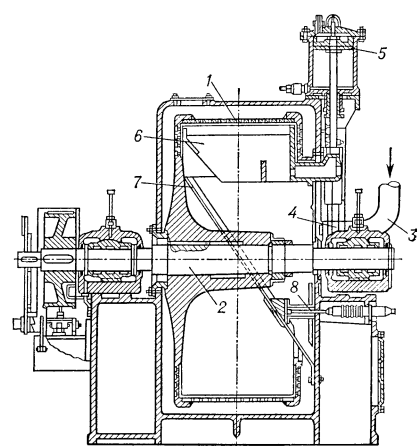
Разрез горизонтальной автоматической фильтрующей центрифуги: 1 — ротор; 2 — горизонтальный вал; 3 — труба для подачи суспензии; 4 — клапан для периодической подачи суспензии; 5 — масляный цилиндр для автоматического подъёма и опускания ножа; 6 — нож для срезания слоя осадка; 7 — желоб для удаления осадка; 8 — вибратор.
